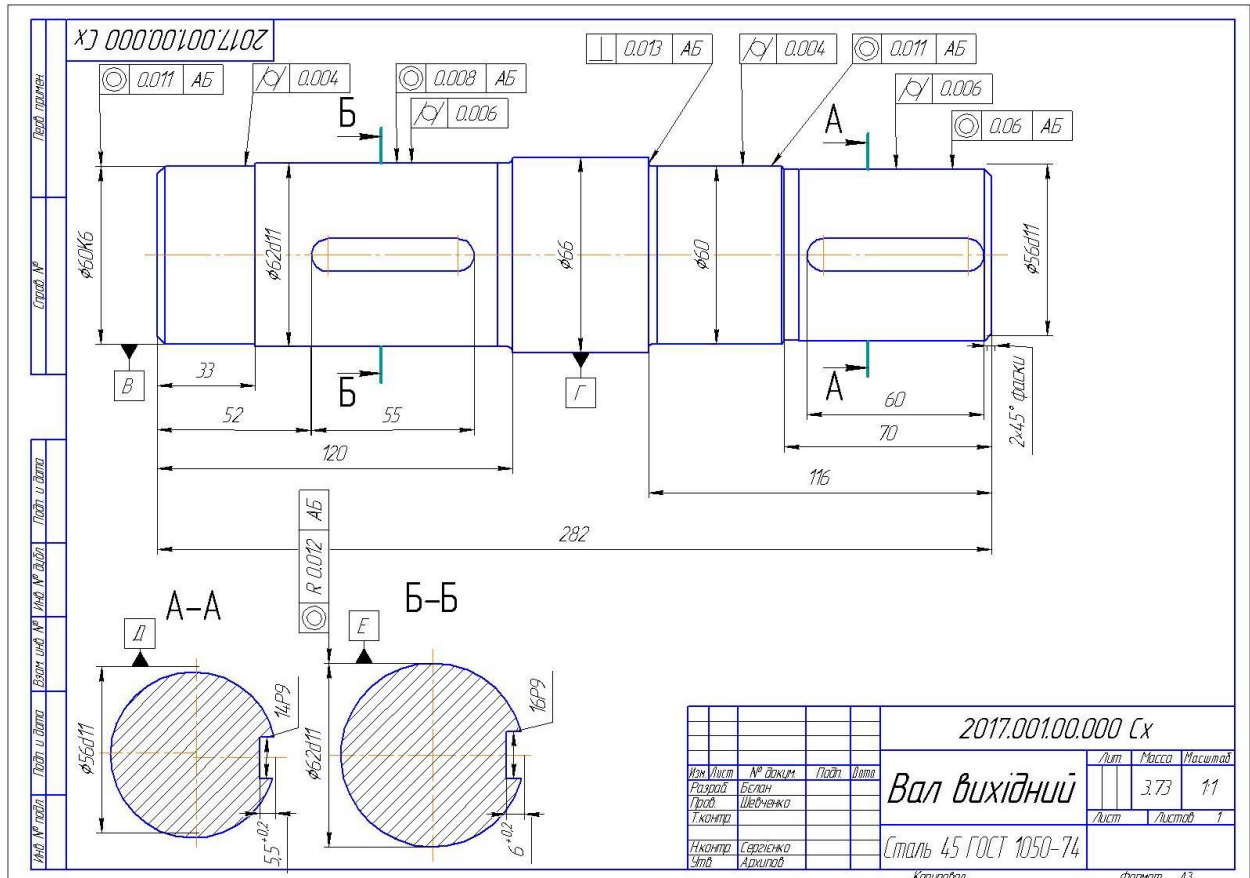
Робоче креслення деталі “вал” з позначенням усіх поверхонь, що піддаються механічній обробці
